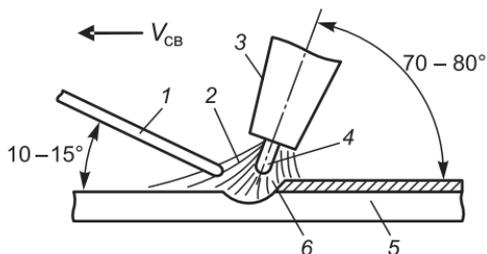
Схема дуговой сварки неплавящимся электродом (TIG)
